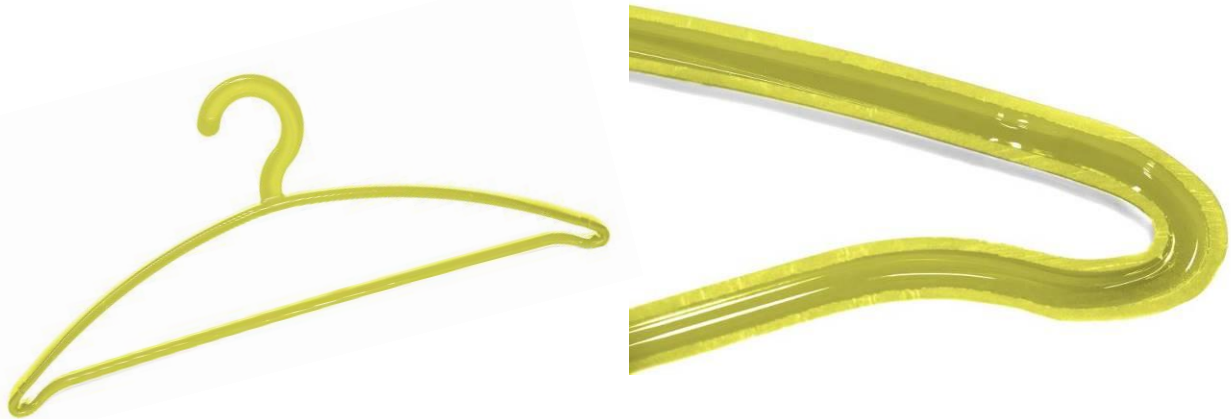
+ b: Cintre produit avec la technologie AIRMOULD® (à gauche) + coupe transversale en gros plan.
